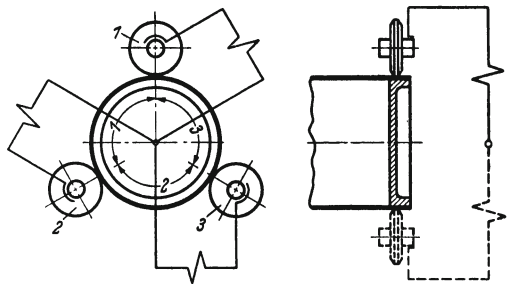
Dreierrollenahtschweißmaschine. Jede Rolle schweißt ein Drittel des Umfanges. Der einzuschweißende Boden bildet die Mittelelektrode.
